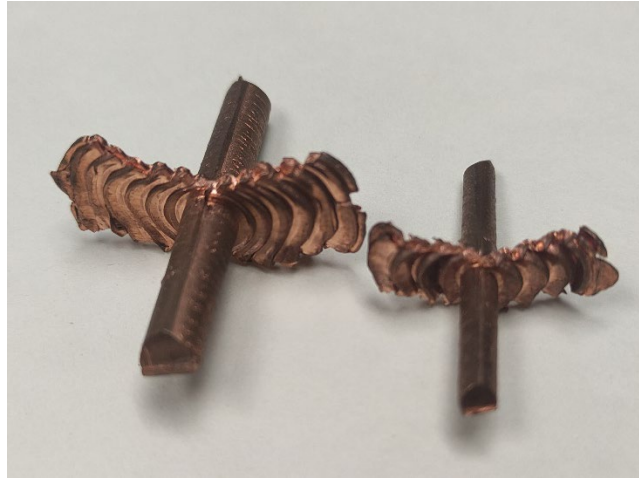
Muestras Soldadas proporcionadas por el fabricante.
